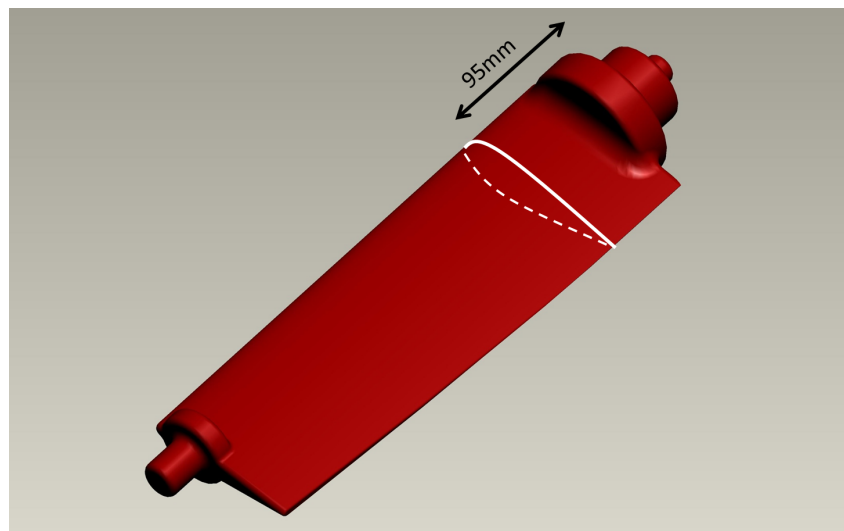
Rappresentazione tridimensionale della paletta oggetto di studio
